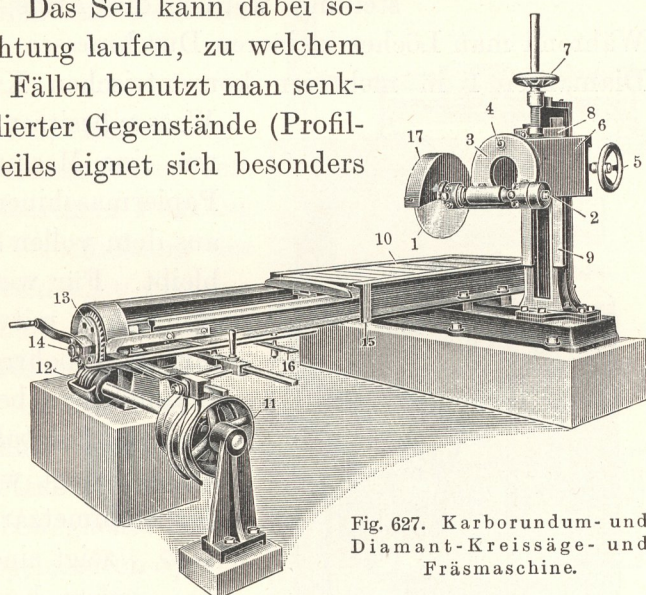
Karborundum- und Diamant-Kreissäge- und Fräsmaschine.
